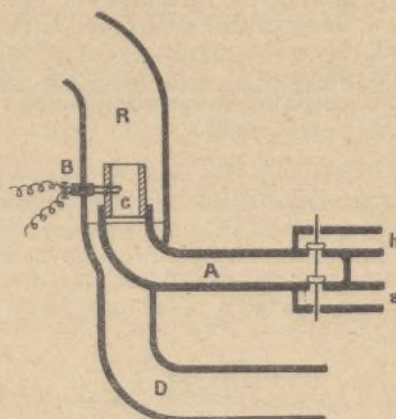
Detalle de la turbina de la Kerr Turbine Company.
